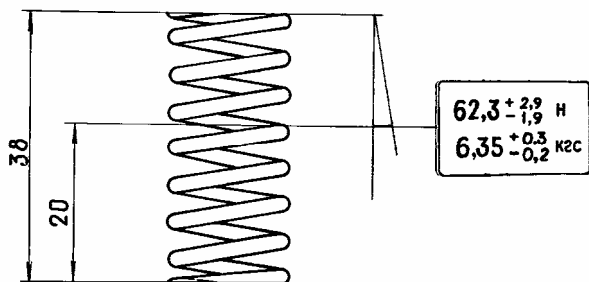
Основные данные для проверки пружины редукционного клапана
